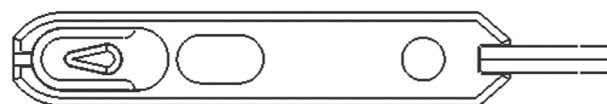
Плоский штырь стягивающего палубного устройства речного звена
